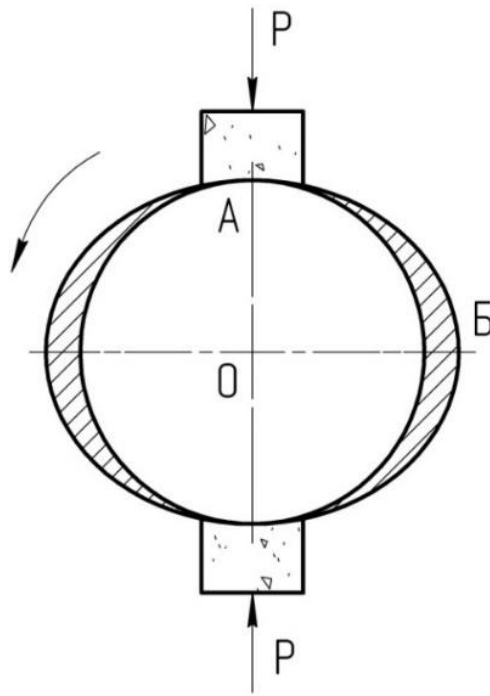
Схема обробки циліндричної поверхні абразивними брусками притисненими з двох сторін
